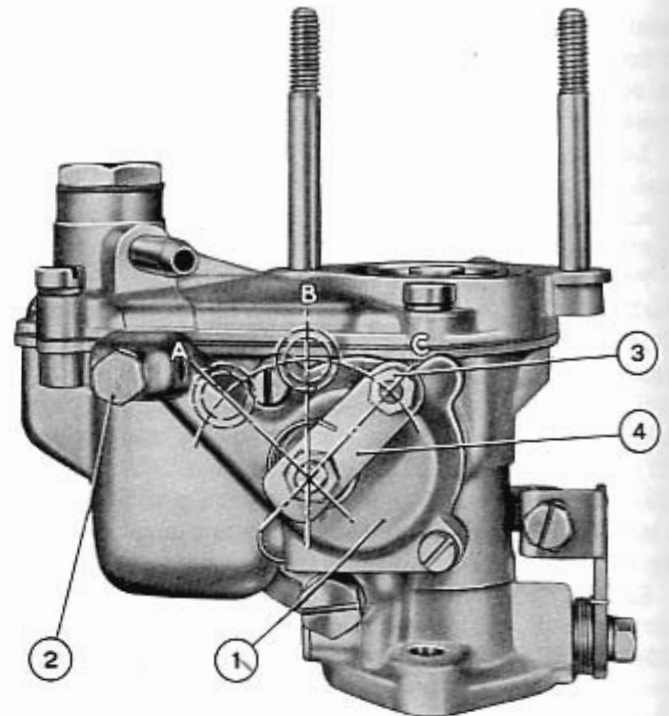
Carburateur Weber 26 IMB 1, côté commande du dispositif de starter.
